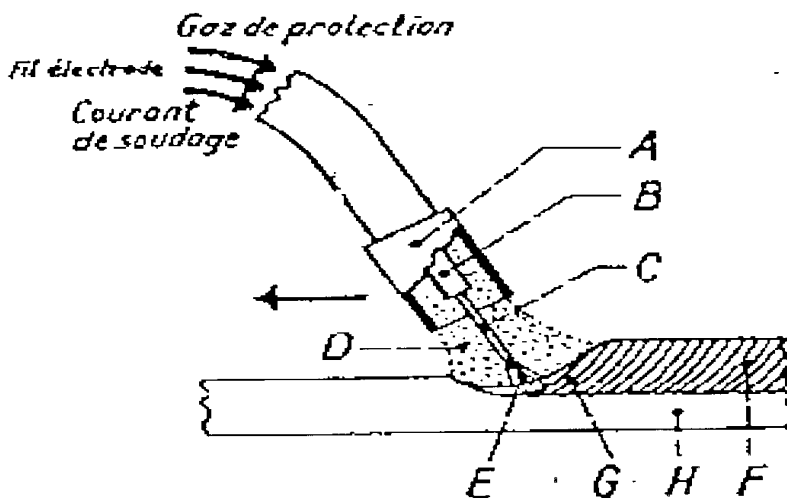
A-tub; B-guia fil; C-electrode-fil; D-gas protector; E-arc; F-cordó de soldadura; G-bany fusió; H-metall base
